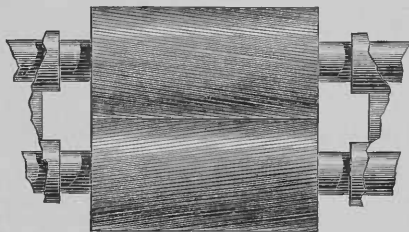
Vue en plan des cylindres striés du broyeur.
